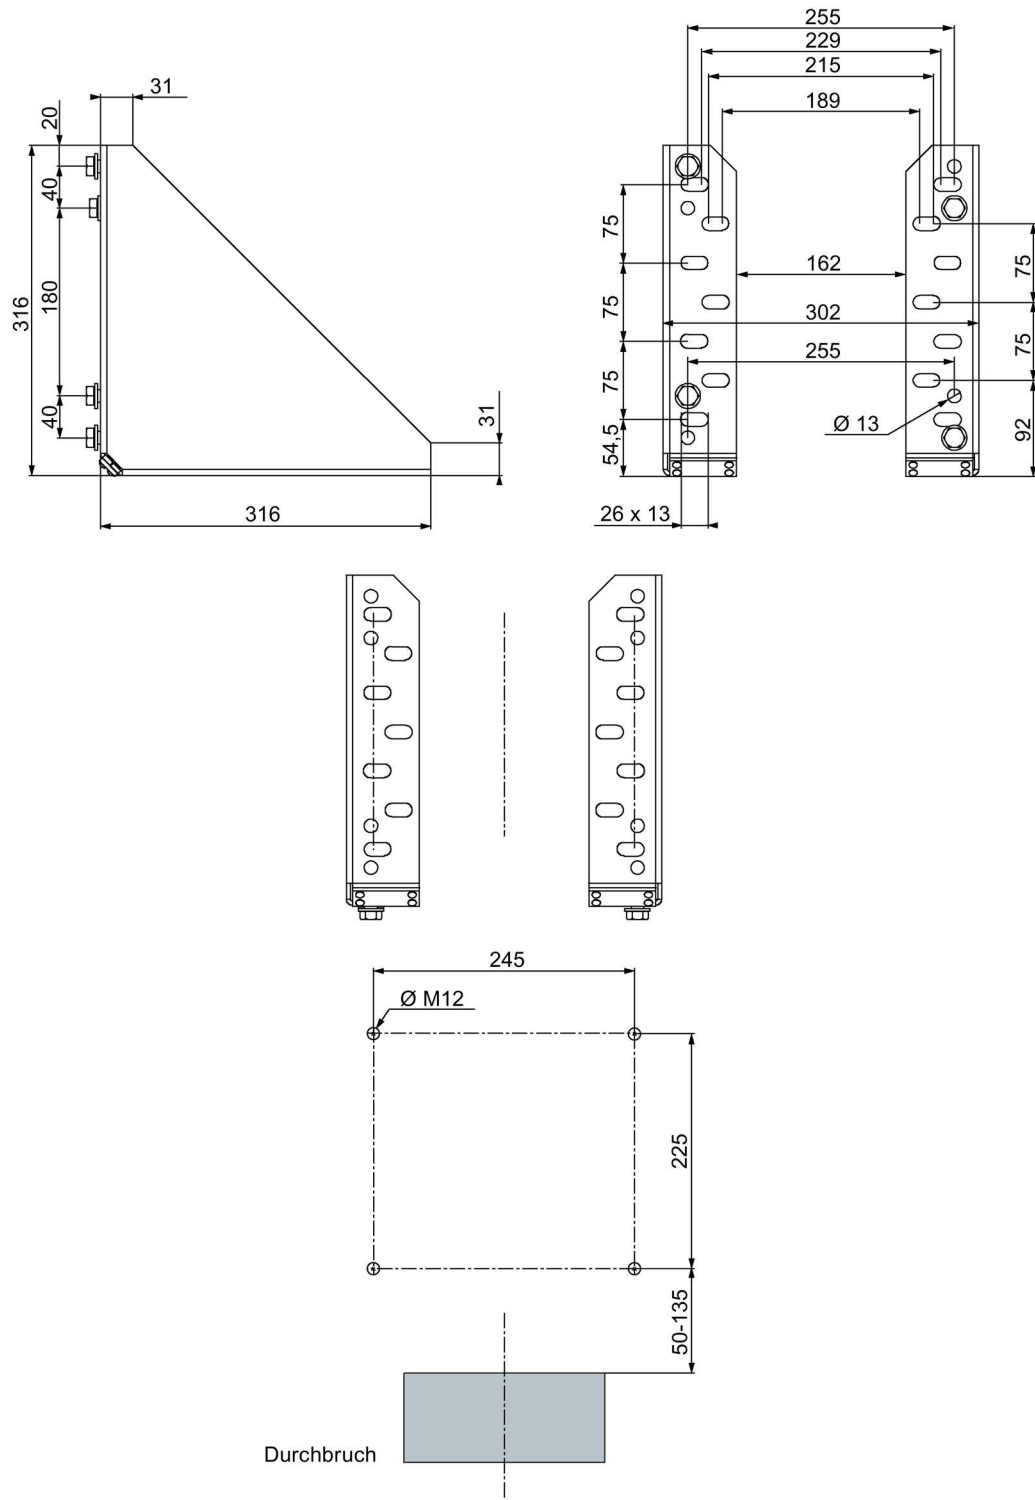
LI-Z-BVD-SB mit Bohrplan
